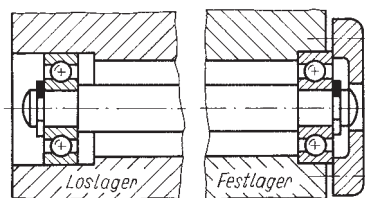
Prinzipieller Aufbau einer Wälzlagerung mit Fest- und Los-Lager
